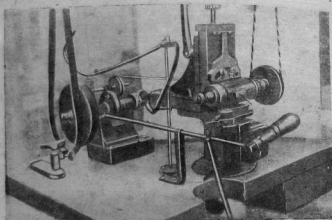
Станок Салаз для фрезеровки пазов в платинках и мостиках.
